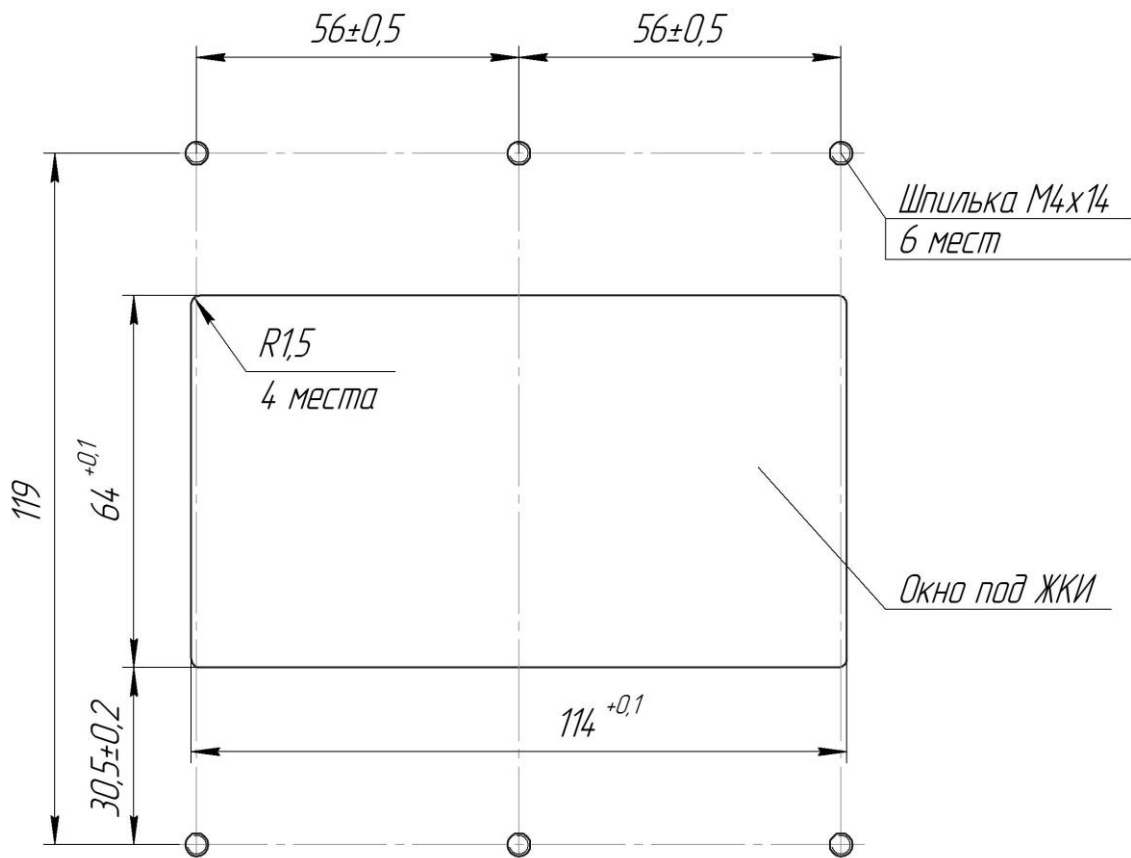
Разметка для крепления ЖКИ (вид со стороны установки ЖКИ)
